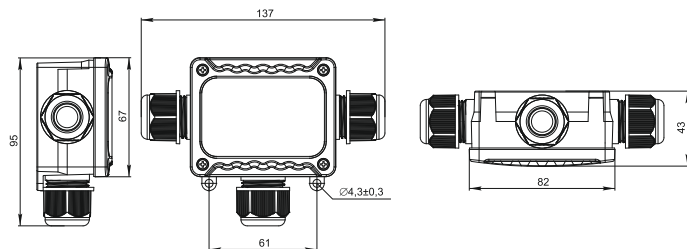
Габаритные размеры коробки WTP-402 / Figure 2 – Overall dimensions of the WTP-402 box
